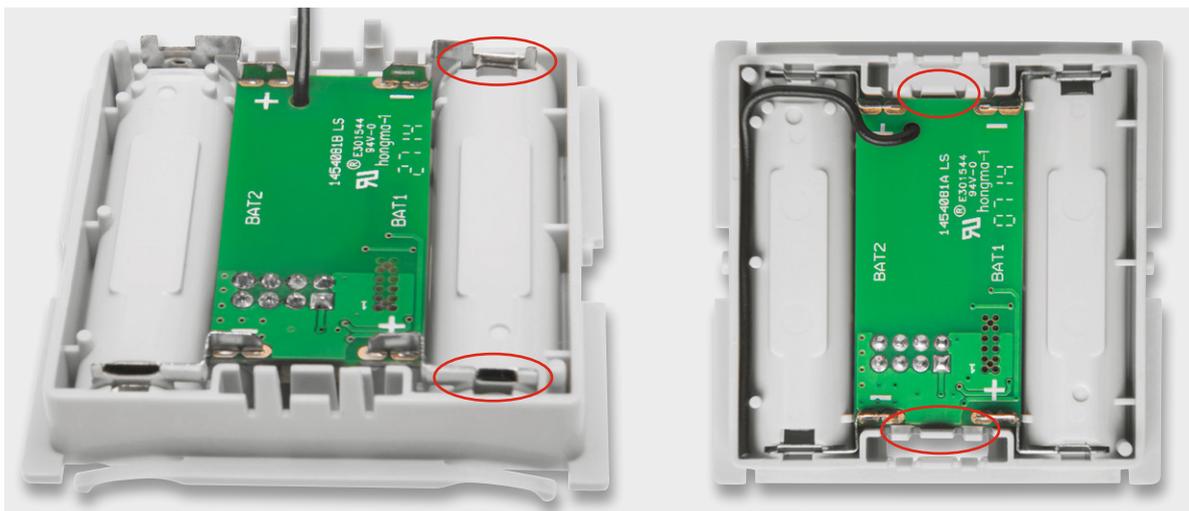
So wird die komplett bestückte Funkplatine eingelegt, die markierten Platinenhalter müssen einrasten. Rechts ist auch die endgültige Lage der Antenne zu sehen.
